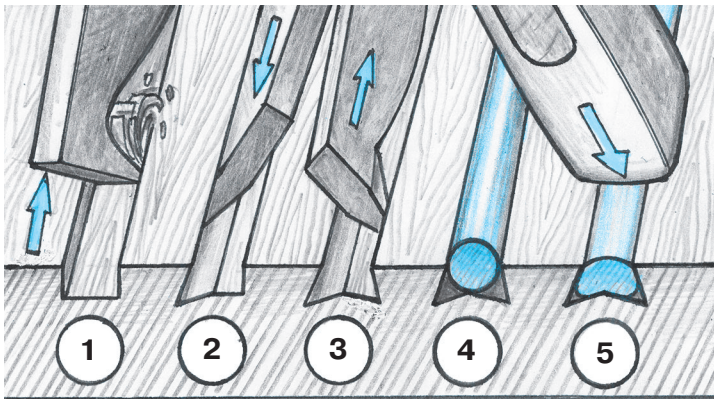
Этапы тауширования: 1 — прорезка; 2, 3 — подрезка; 4 — укладка проволоки; 5 — забивка проволоки.
